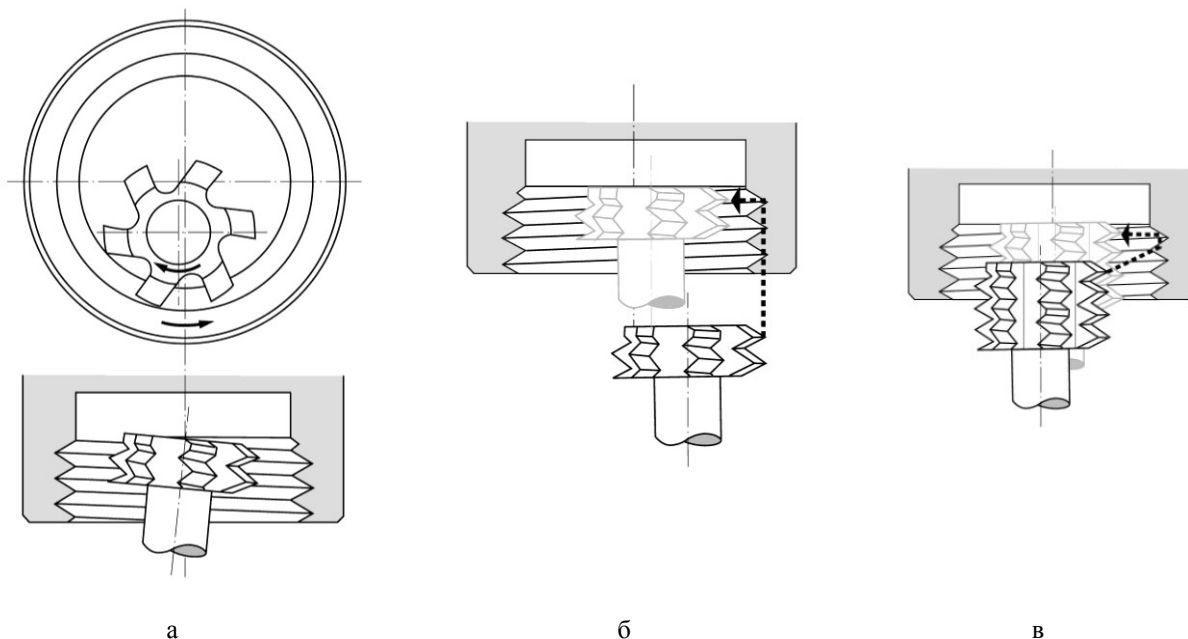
Схемы токарно-фрезерной обработки внутренней резьбы: а - с наклонной осью инструмента при продольном перемещении вдоль оси резьбы (*Traversing method*), б - с параллельными осями при продольном перемещении вдоль оси резьбы (*Traversing method*), в - с параллельными осями и обработкой сразу по всей длине резьбы (*Plunge method*).
